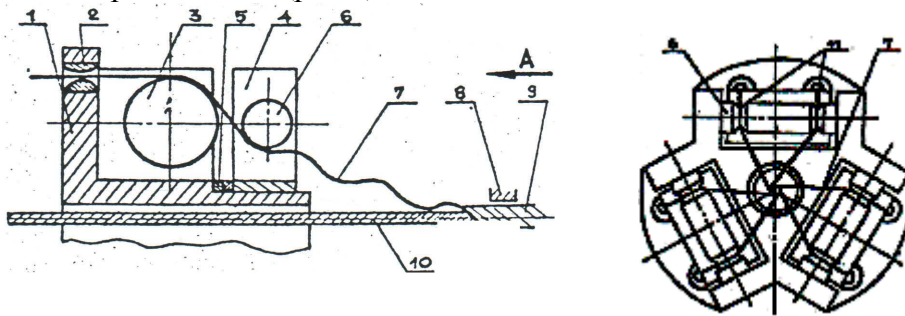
Загальний вид преформатора на опорах кочення з схемою преформування елементів крученого виробу
